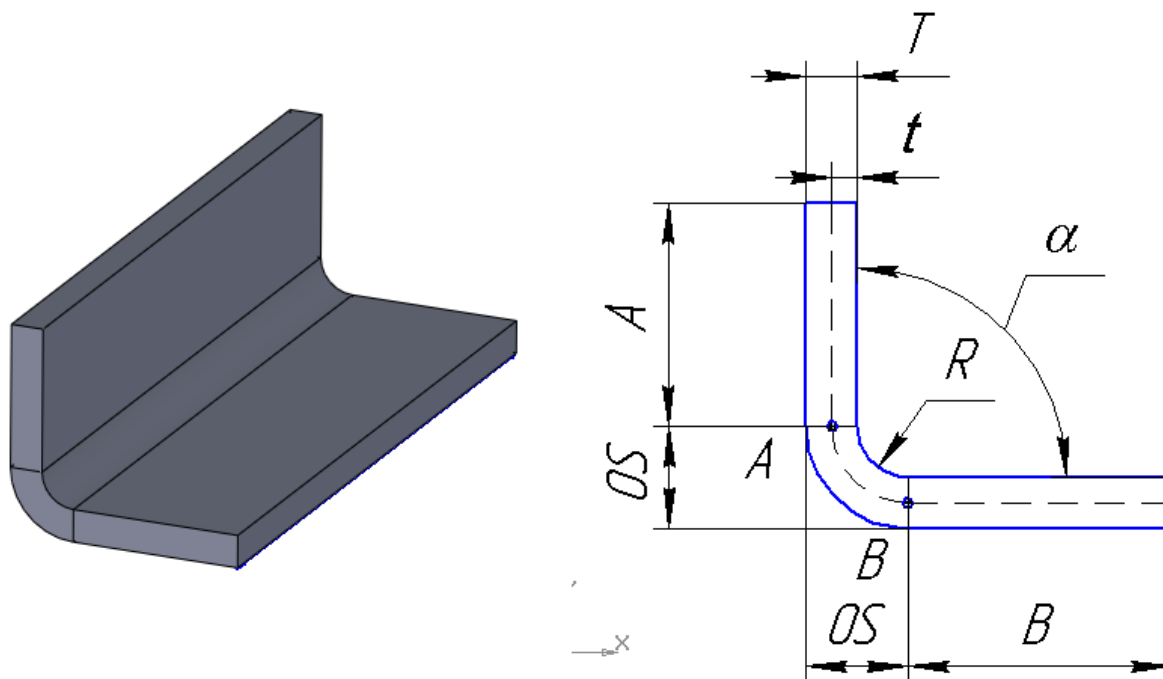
Определение допуска сгиба листового металла
